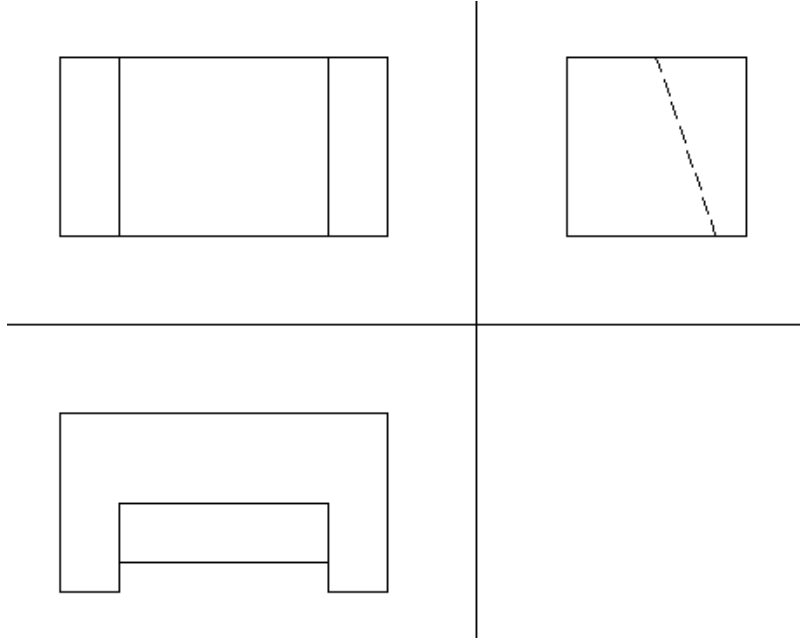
Temel boyutların profil düzlemine taşınması
